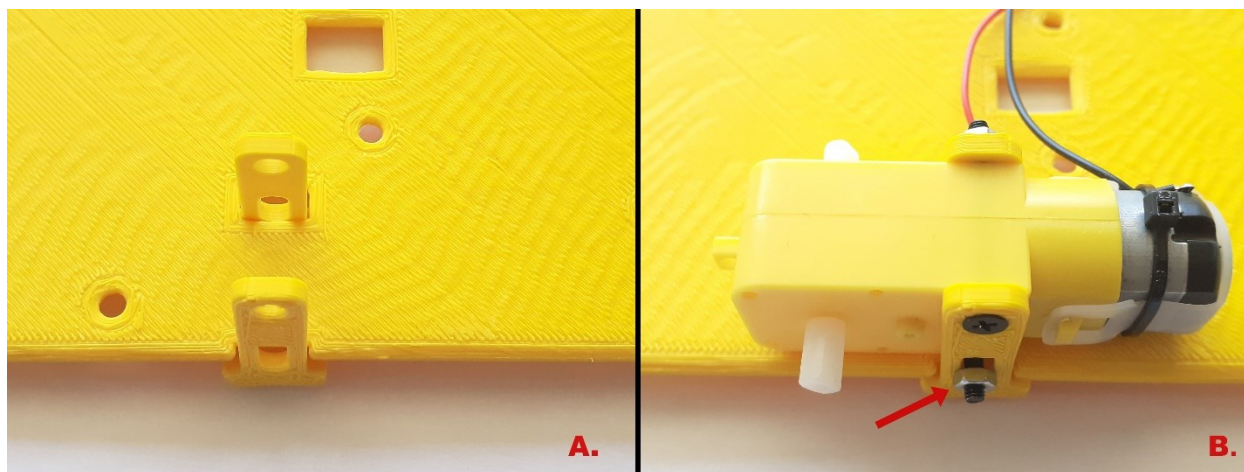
A. Colocação dos 2 braços no chassis? B. Estabilizar o motor com os 2 parafusos de 30 mm e as 2 porcas
